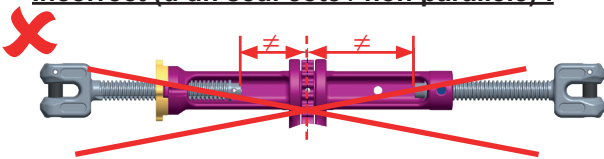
Serrage ou desserrage incorrect (d'un seul côté non parallèle)
